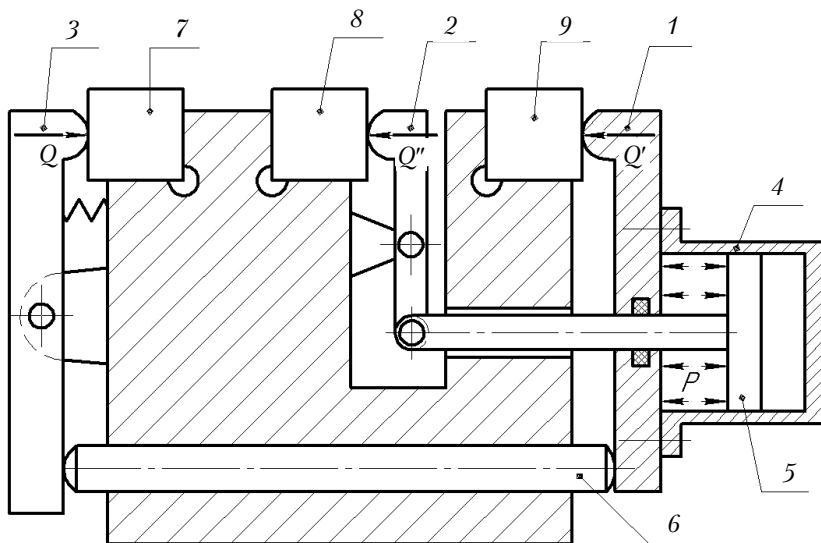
Схема много местного зажима с плавающим гидроцилиндром
